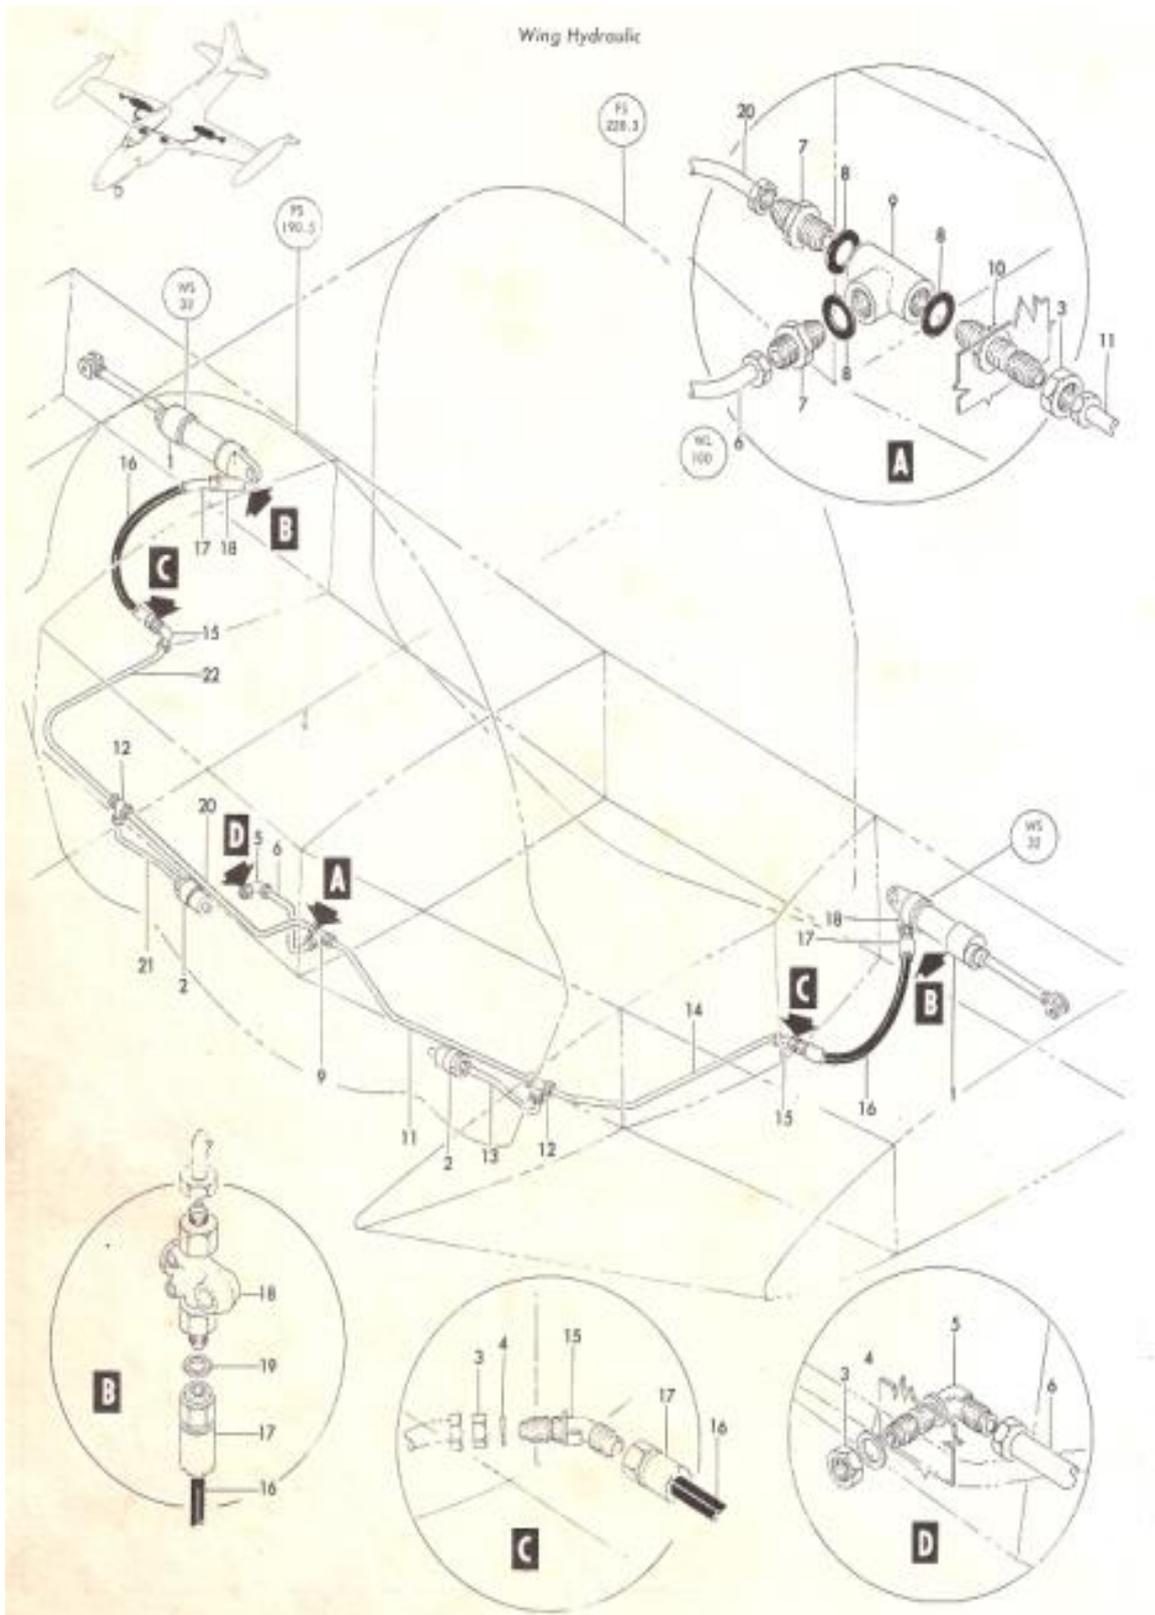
Cañerías de las Puertas Internas y el Tren Aterrizaje Principal
